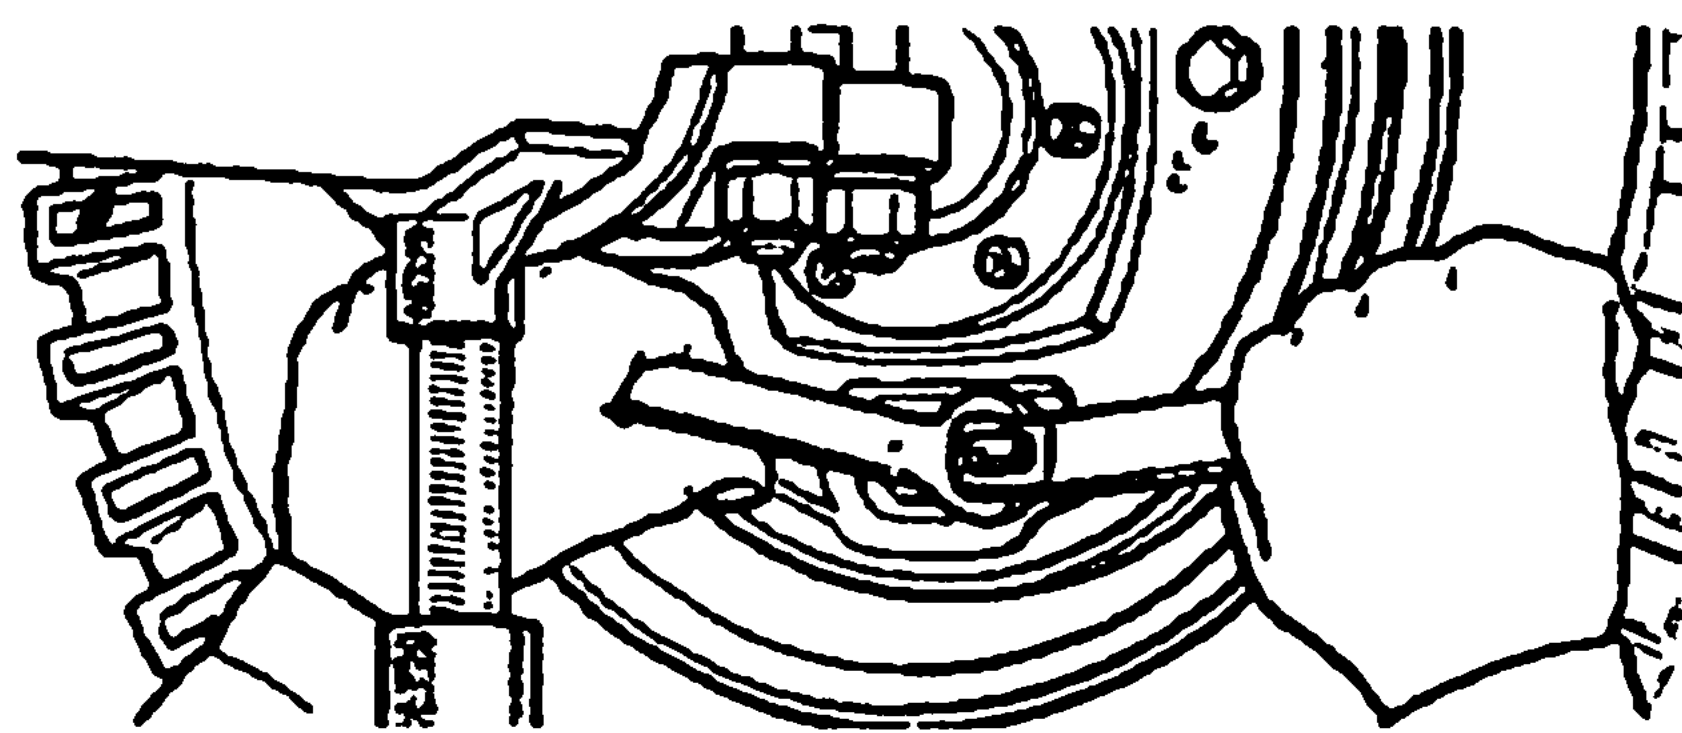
Регулировка тормозных колодок заднего колеса с помощью опорных пальцев
